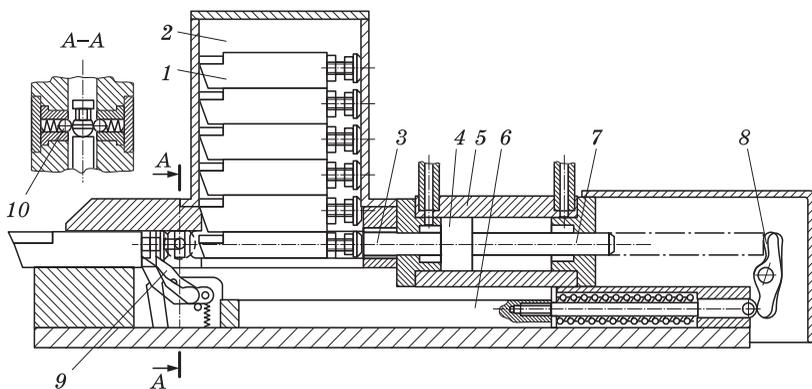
Схема устройства для автоматической замены проходных резцов
